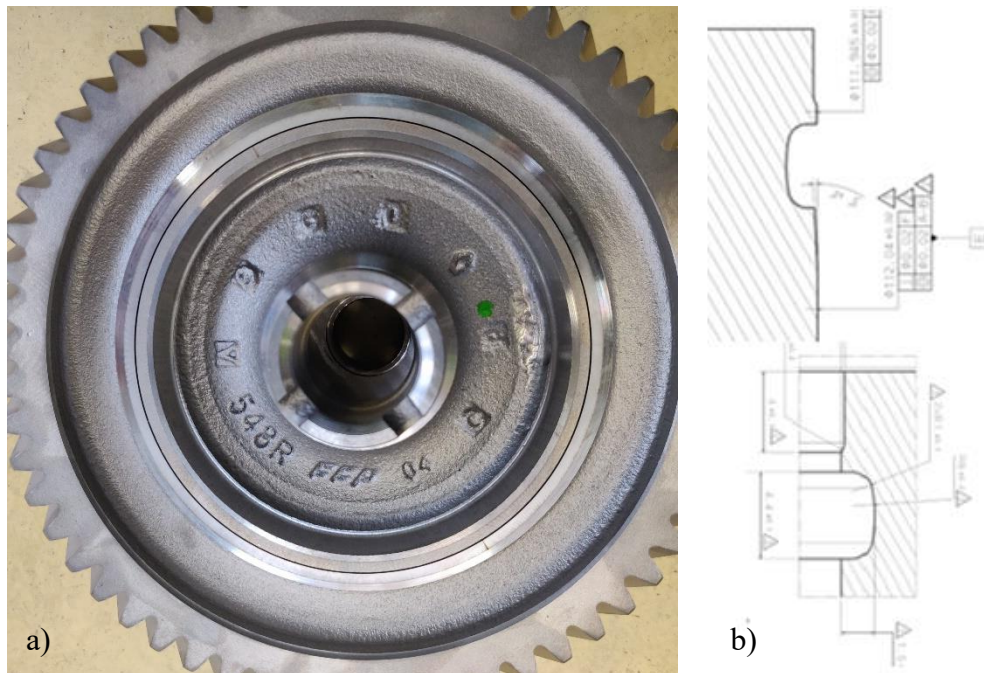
a) Conjunto prensado pré-soldadura; b) Configuração da junta.
